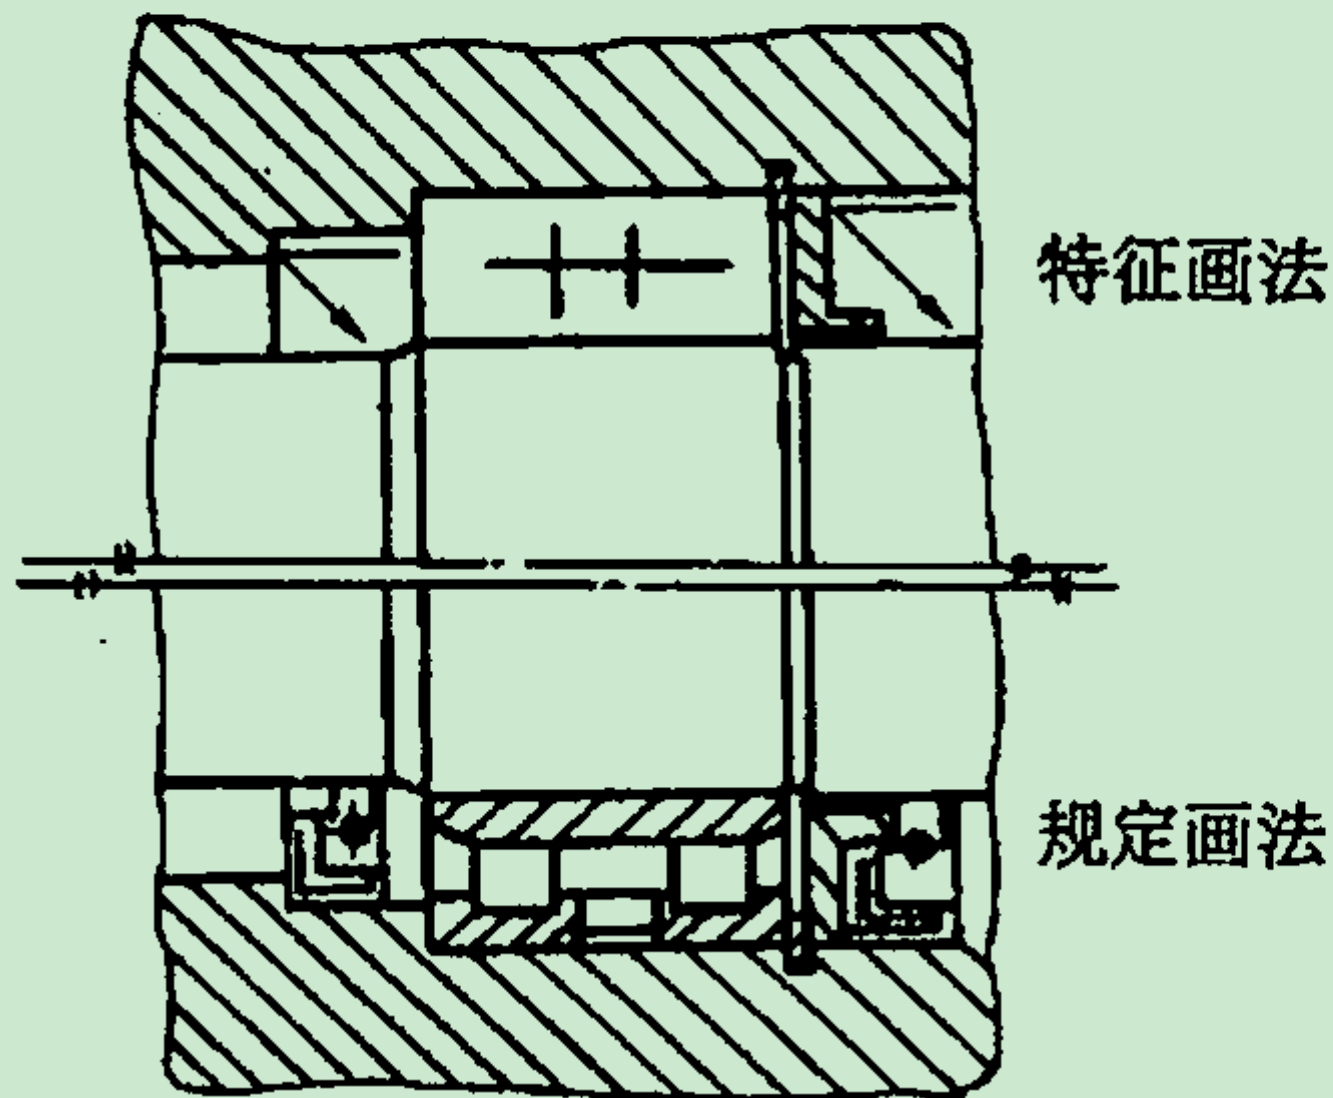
双列圆柱滚子轴承在装配图中的画法
